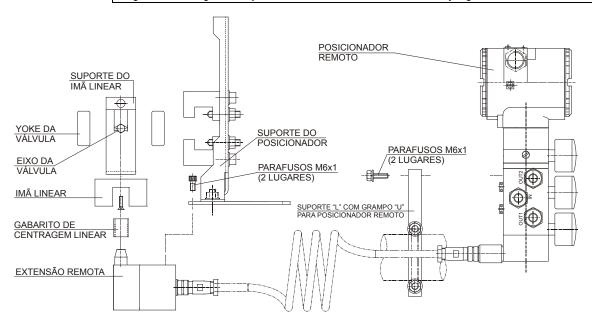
Posicionador em Atuador Linear com Sensor de Posição Remoto
